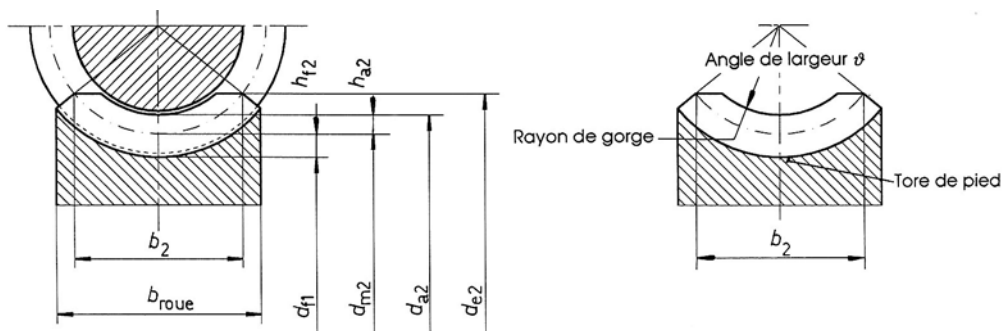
Forme et dimensions diamétrales de la roue à vis
